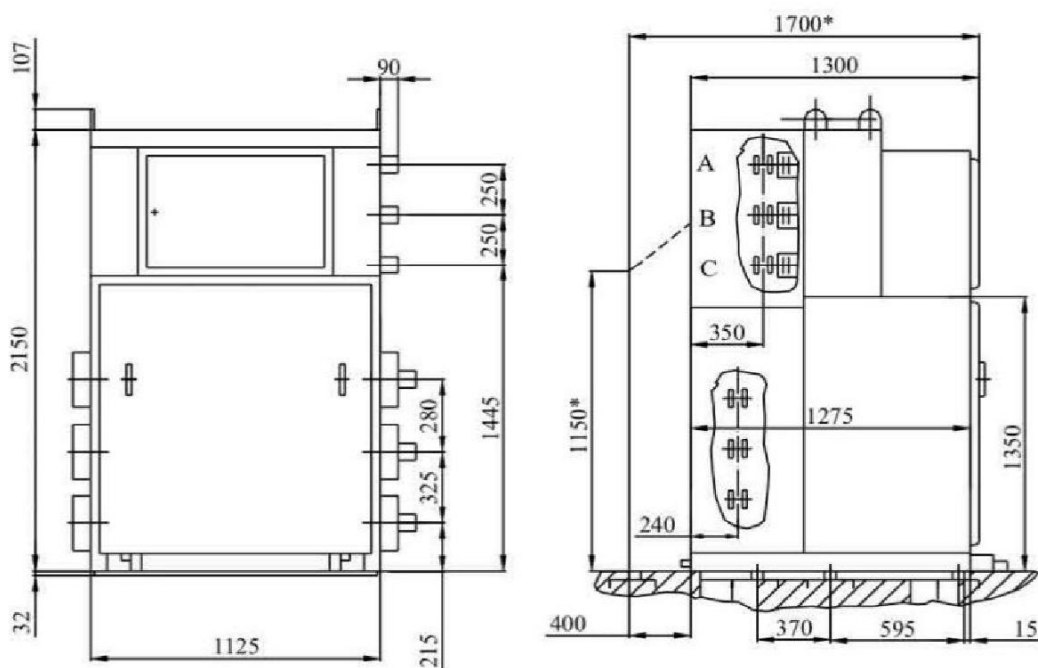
Габаритные, установочные и присоединительные размеры шкафов КРУ серии КМ-1Ф на токи 2000...3150 А
